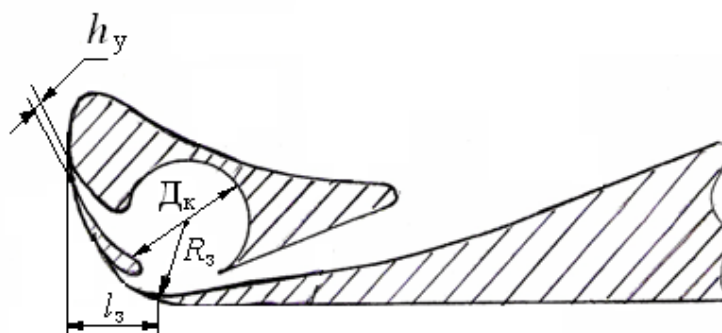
Схема вихревой камеры лопатки рабочего колеса центробежного вентилятора
